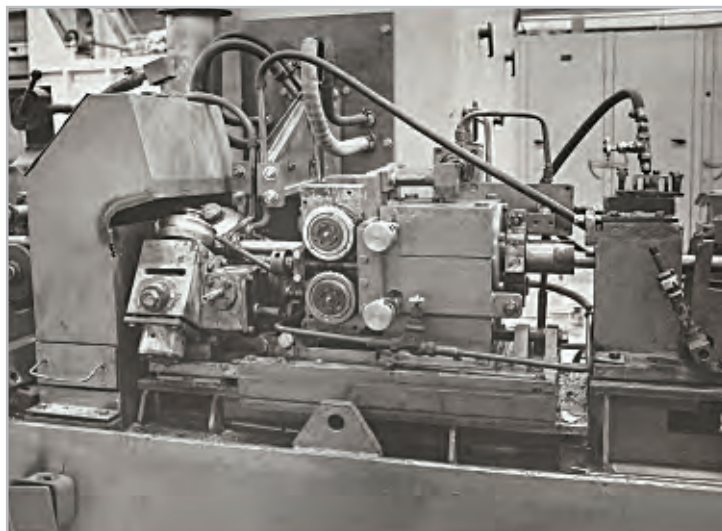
Сварочная и ножевая клетки с устройством для улавливания «выплесков» металла
